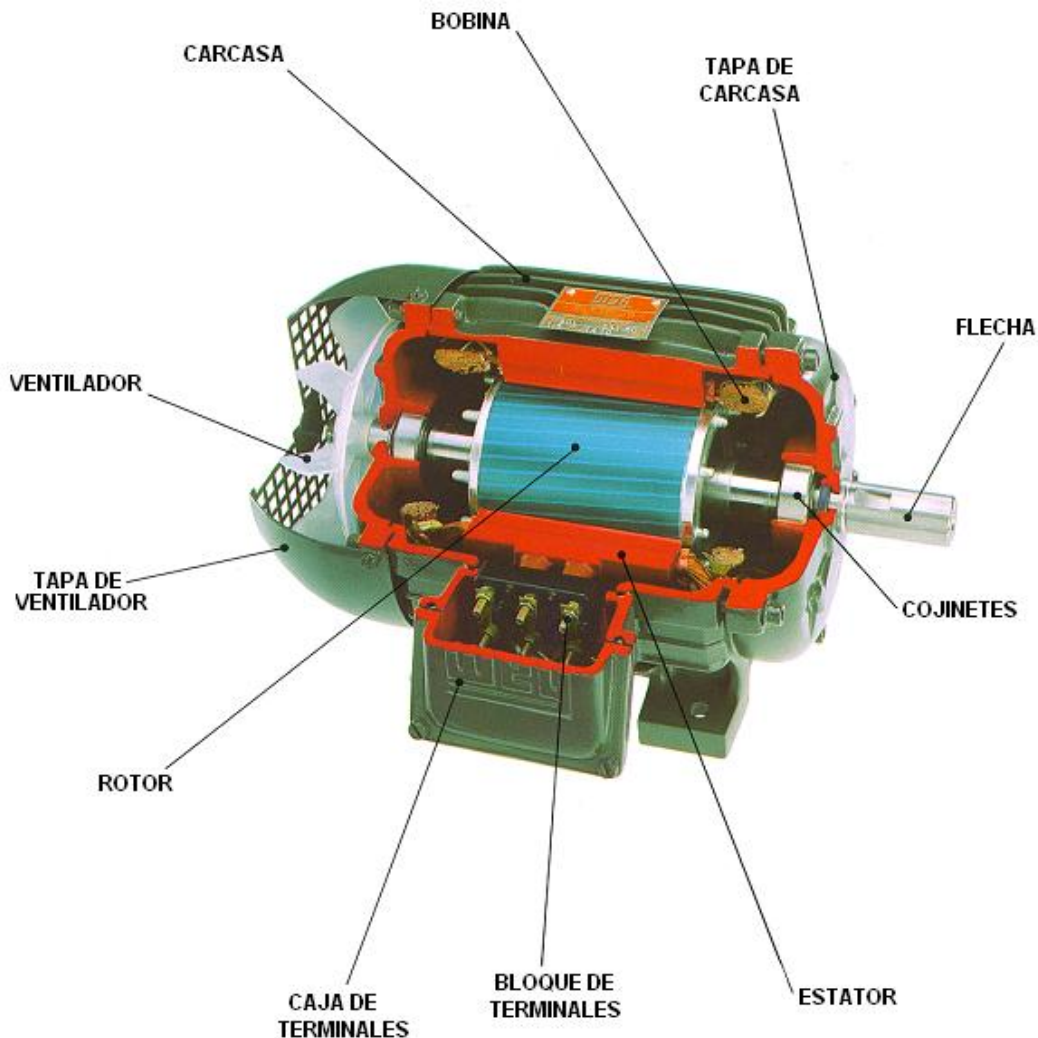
Partes de un motor de Inducción de Corriente Alterna
